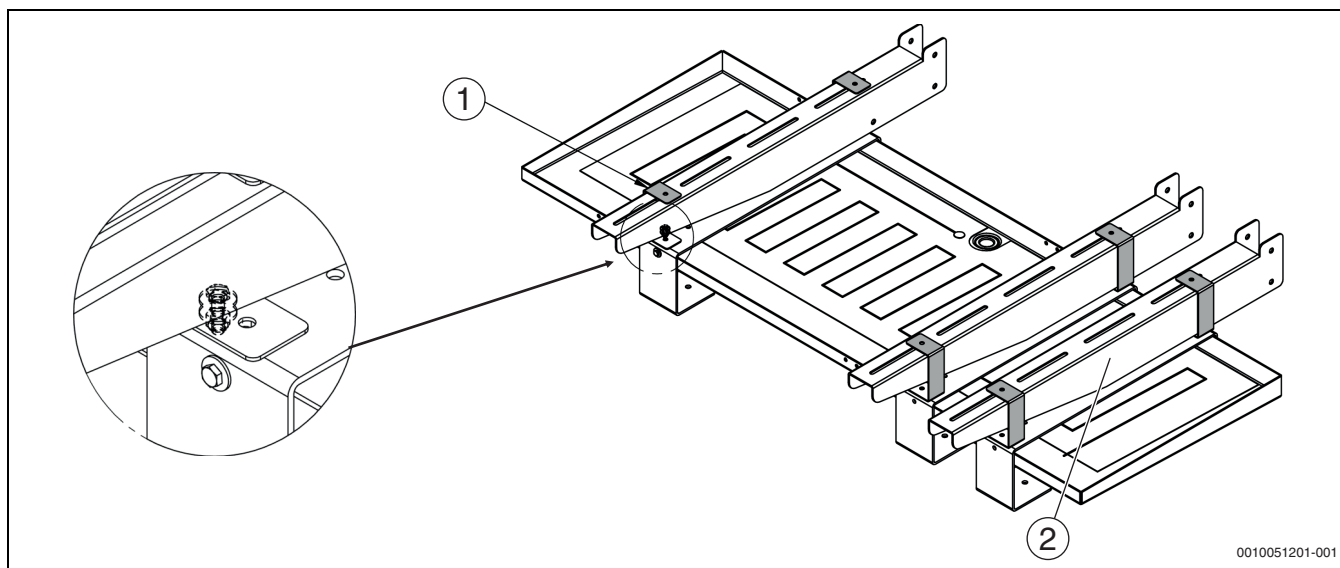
Installazione alla parete del kit dei supporti di fissaggio
